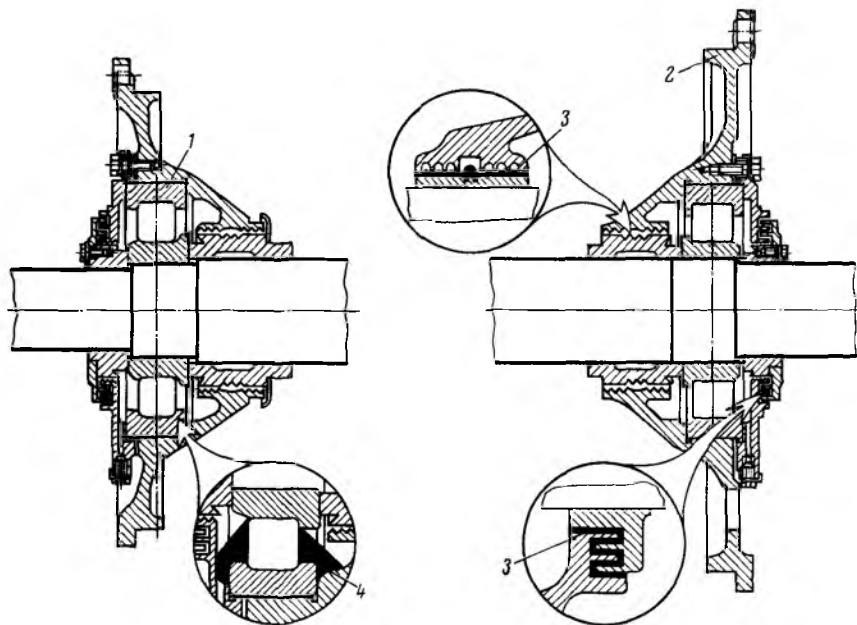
Установка роликовых подшипников в тяговых двигателях:
